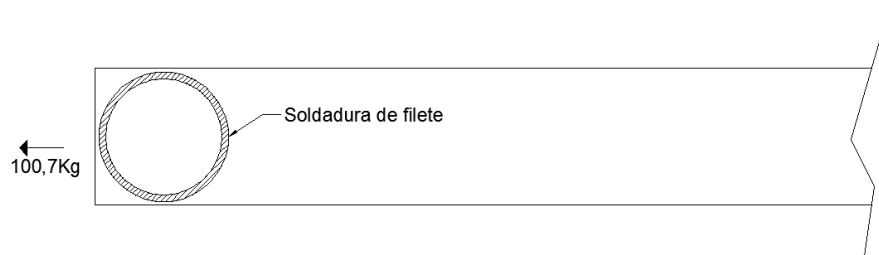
(Soldadura de la base del pórtico)
